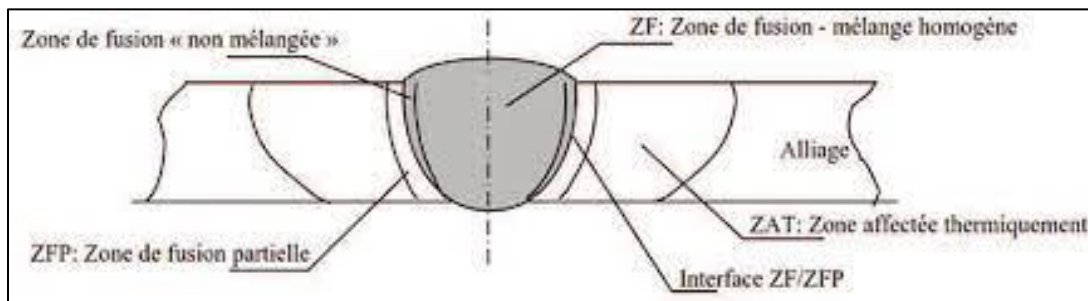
les zone du cordon de soudure en soudage [19].
